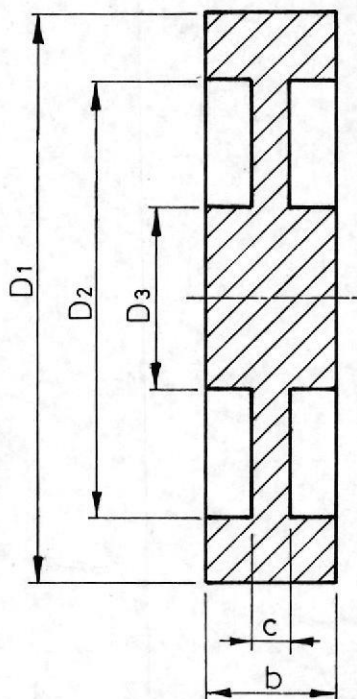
DIMENSIONES DEL VOLANTE
